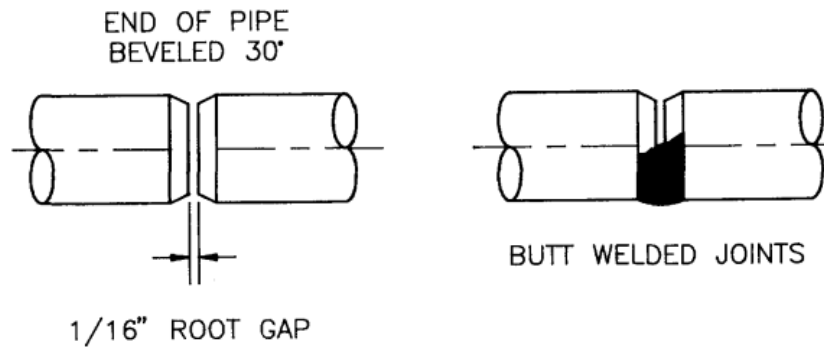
Joints soudés bout à bout. [1]
